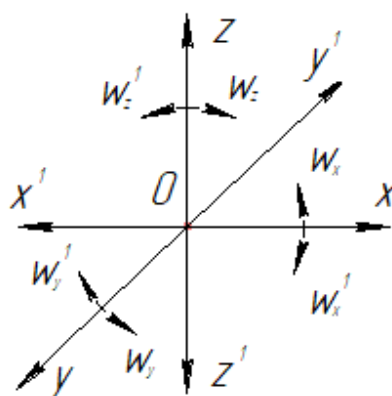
Схема однобічних зв'язків, що покладають на заготовку
